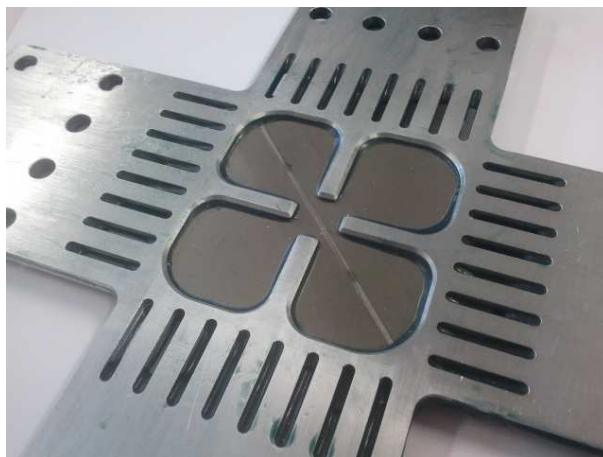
Partie centrale de l'éprouvette avec cordon de soudure.
